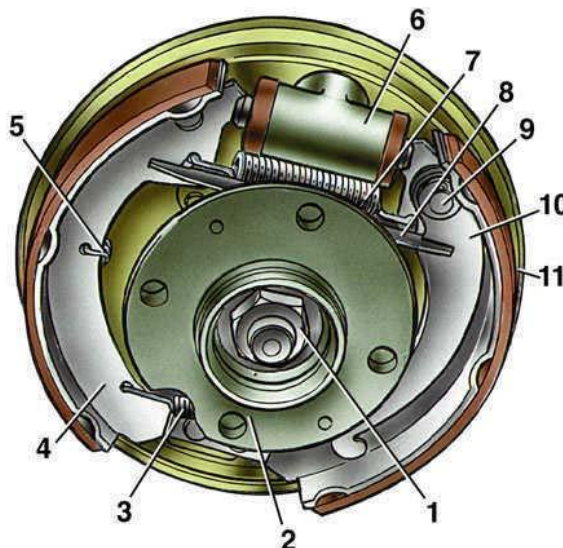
Гальмівний механізм заднього колеса автомобіля ВАЗ 2110: 1 - гайка кріплення
